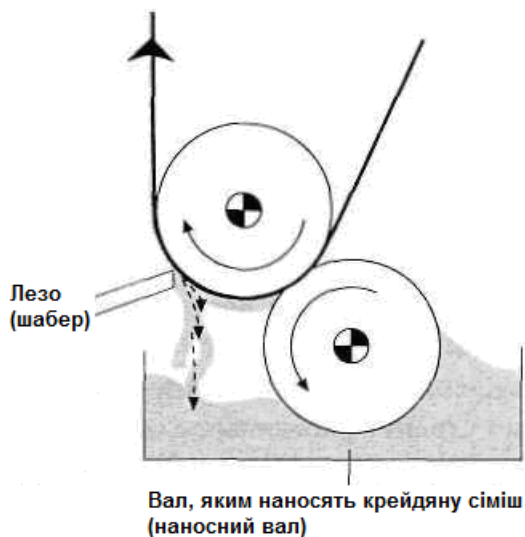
Крейдувальний пристрій з металевим шабером
